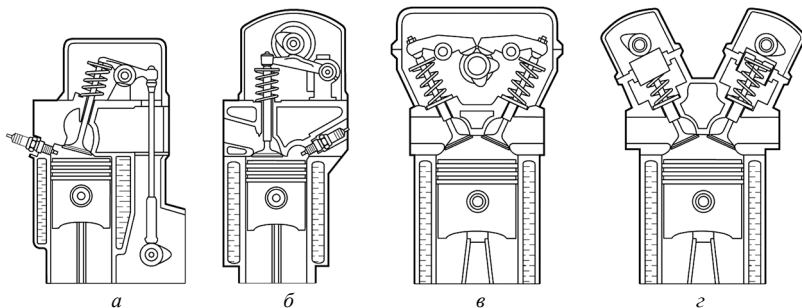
Схемы привода клапанов: *а* – привод клапанов с помощью штанги и коромысла при нижнем расположении распределительного вала; *б* – привод клапанов с помощью рычага при верхнем расположении распределительного вала; *в* – привод клапанов двумя коромыслами от одного распределительного вала; *г* – привод клапанов двумя распределительными валами
